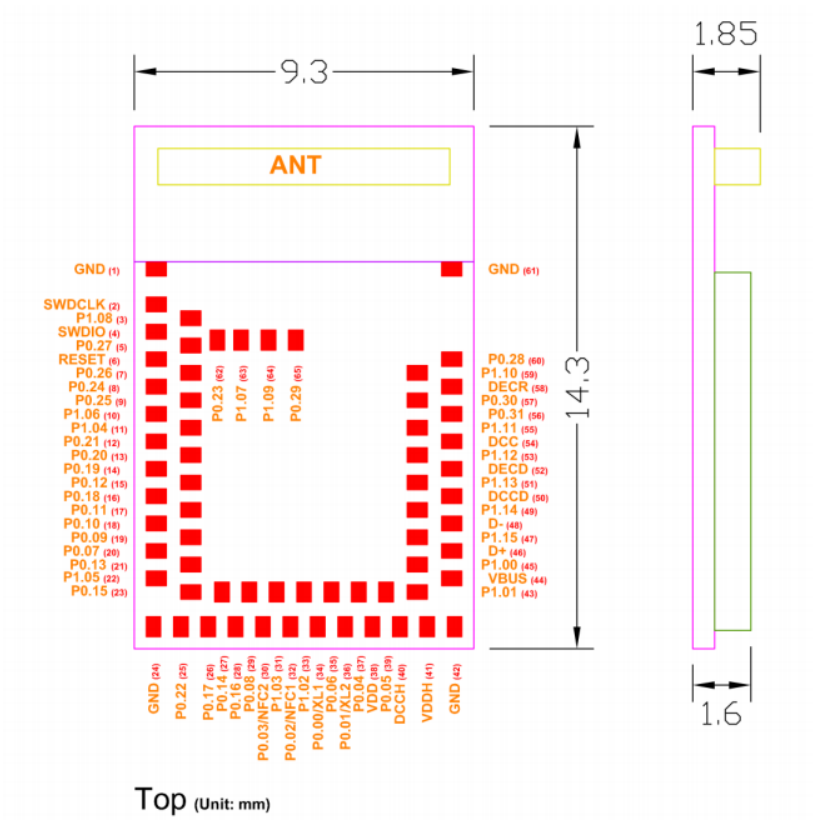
Dimensions de PCB du module MDBT53-1M [151]
